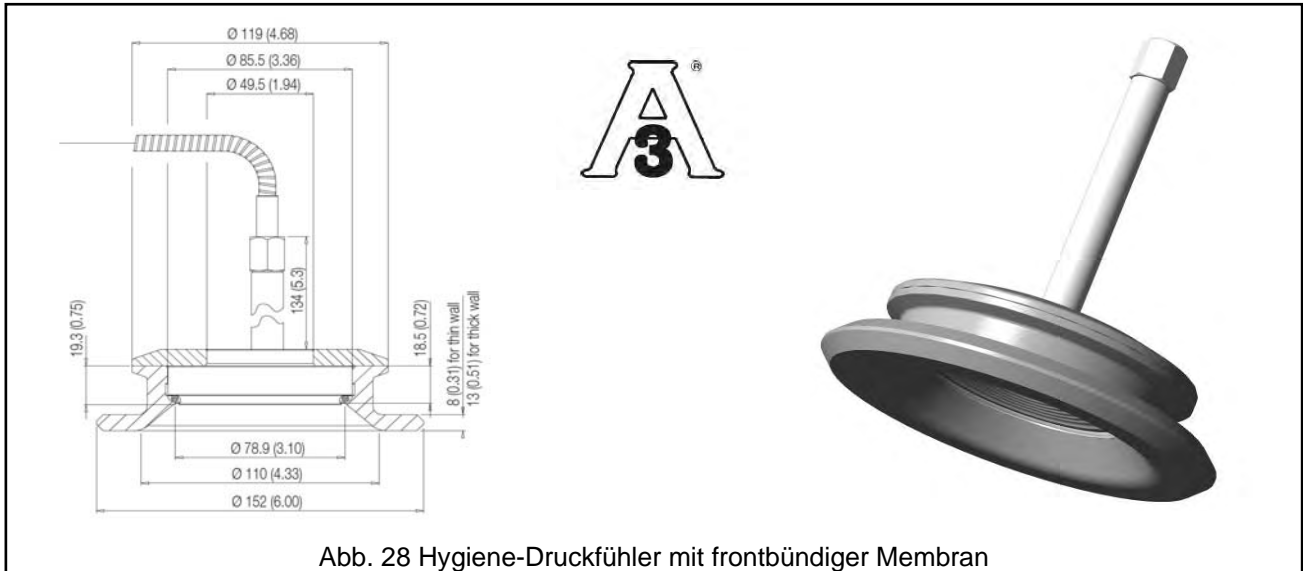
Hygiene-Druckfühler mit frontbündiger Membran
